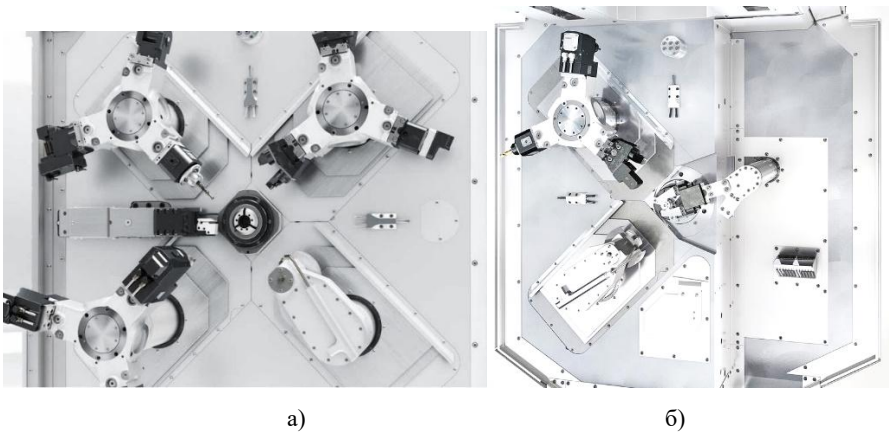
Основний (а) і протишпиндель (б)
